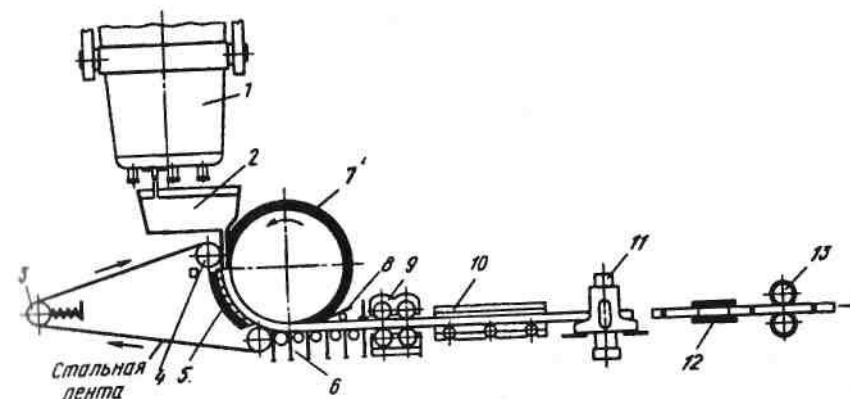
Литейно-прокатный агрегат с роторной УНРС: 1 — сталеразливочный ковш; 2 — промежуточный ковш; 3 — приводной валок; 4 — прижимные валки; 5 — охлаждение ленты; 6 — направляющие ролики; 7 — литейное колесо; 8 — снимающий клин; 9 — тянущие ролики; 10 — печь для выравнивания температуры слитка; 11 — ножницы; 12 — вертикальная прокатная клеть; 13 — горизонтальная прокатная клеть
